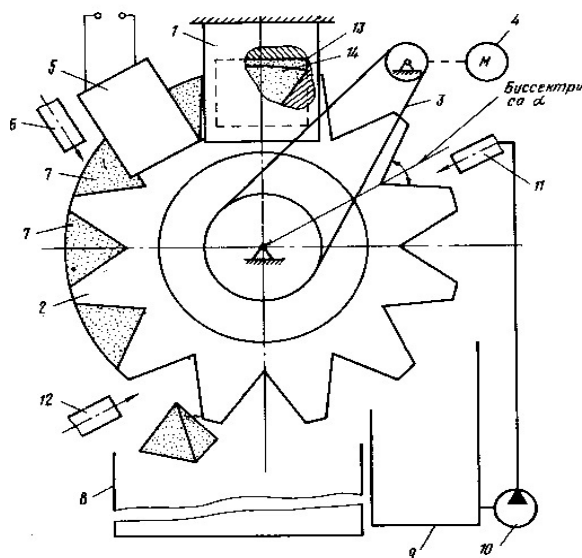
Схема работы устройства для прессования абразивных гранул преимущественно в форме тетраэдра [4]: 1 – фильера; 2 – приводной нож; 3 – клиноременная передача; 4 – электродвигатель; 5 – индуктор ТВЧ; 6 – форсунка; 7 – гранулы; 8 – бункер; 9 – бак с смазывающим материалом; 10 – насос; 11, 12 – форсунки; 13 – основная полость; 14 – дополнительная коническая полость
